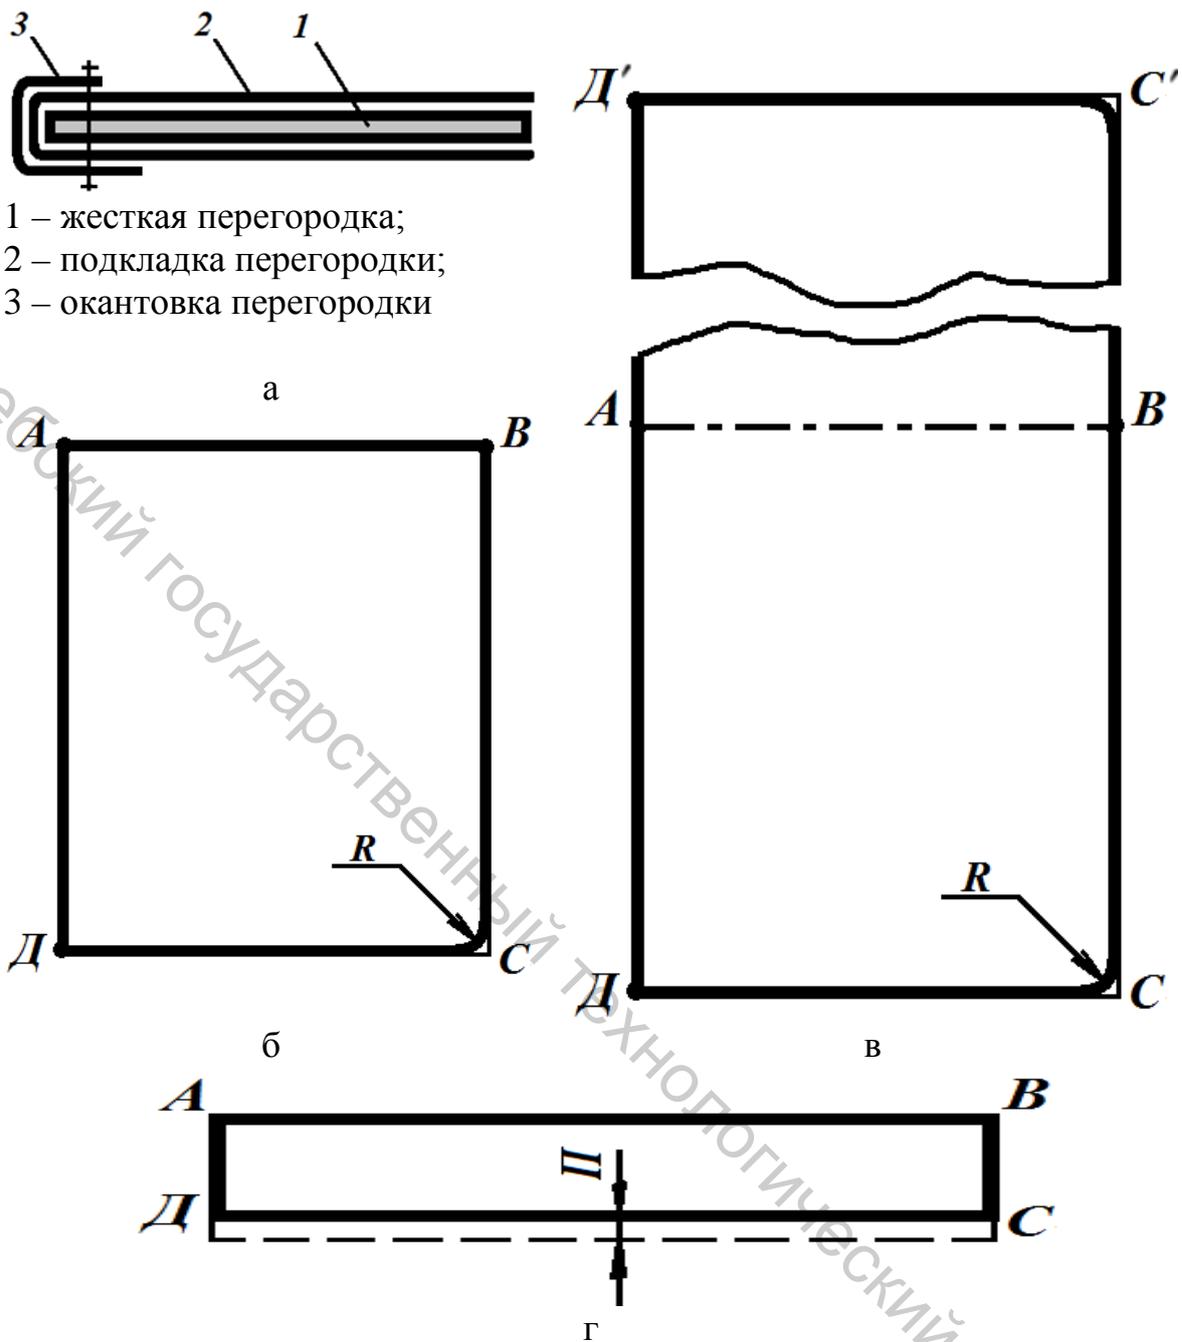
Схема и проектирование перегородки: а – схема перегородки; б – проектирование жесткой перегородки; в – проектирование подкладки перегородки; г – проектирование окантовки для перегородки
